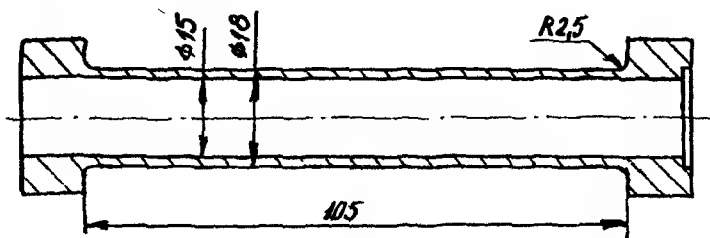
Образец для испытаний на релаксацию напряжений
